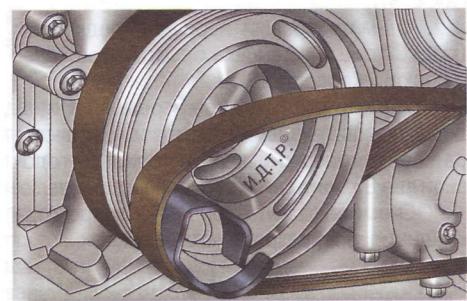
Установка ремня привода компрессора кондиционера на приспособление для его монтажа
